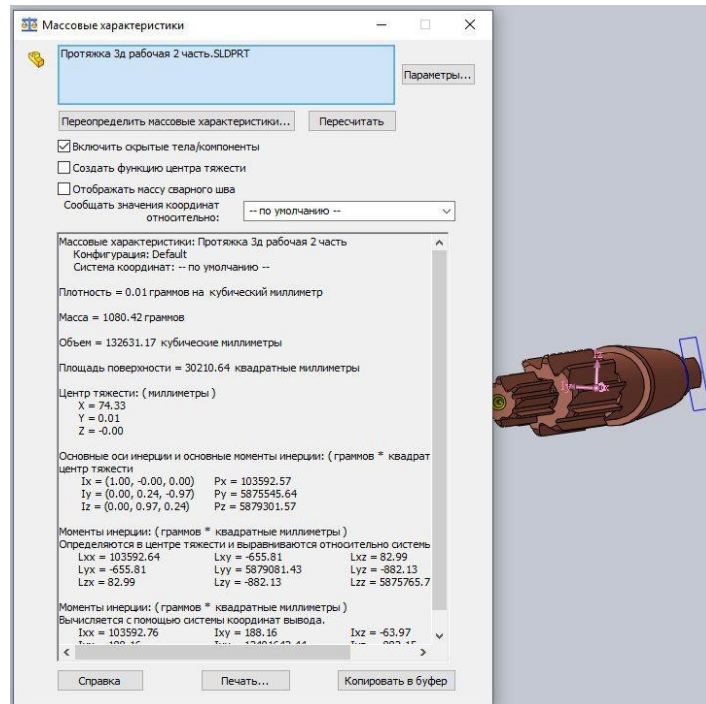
Маса готового інструменту (цільна заготовка)
